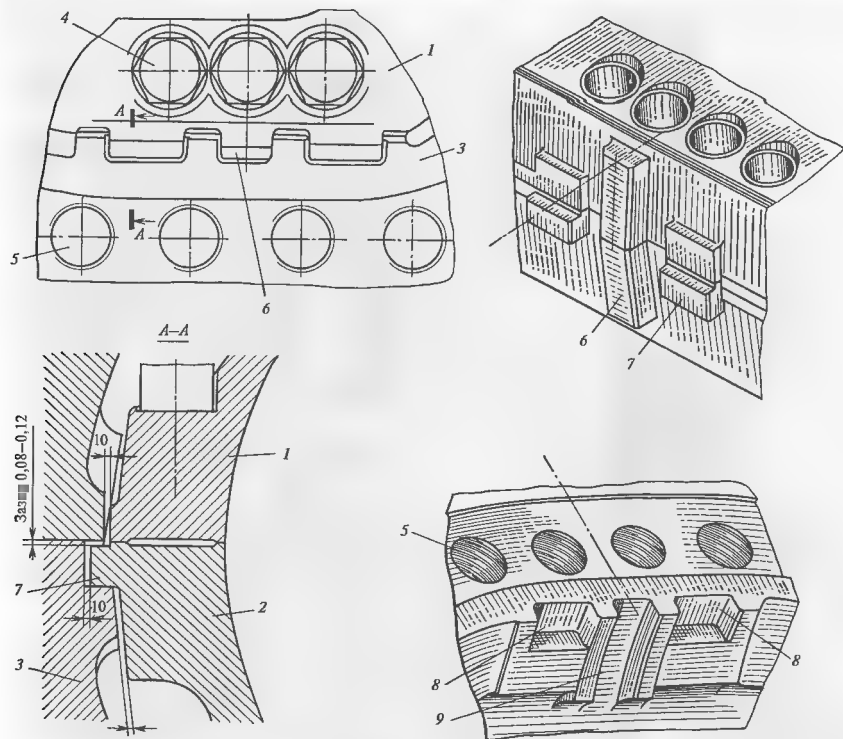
Детали подвески внутреннего корпуса двухстенного ЦВД во внешнем корпусе
